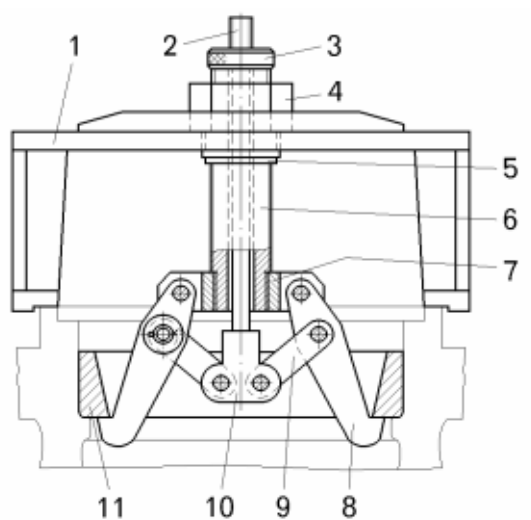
Съемник для выпрессовки наружных колец подшипников ступиц передних колес:
